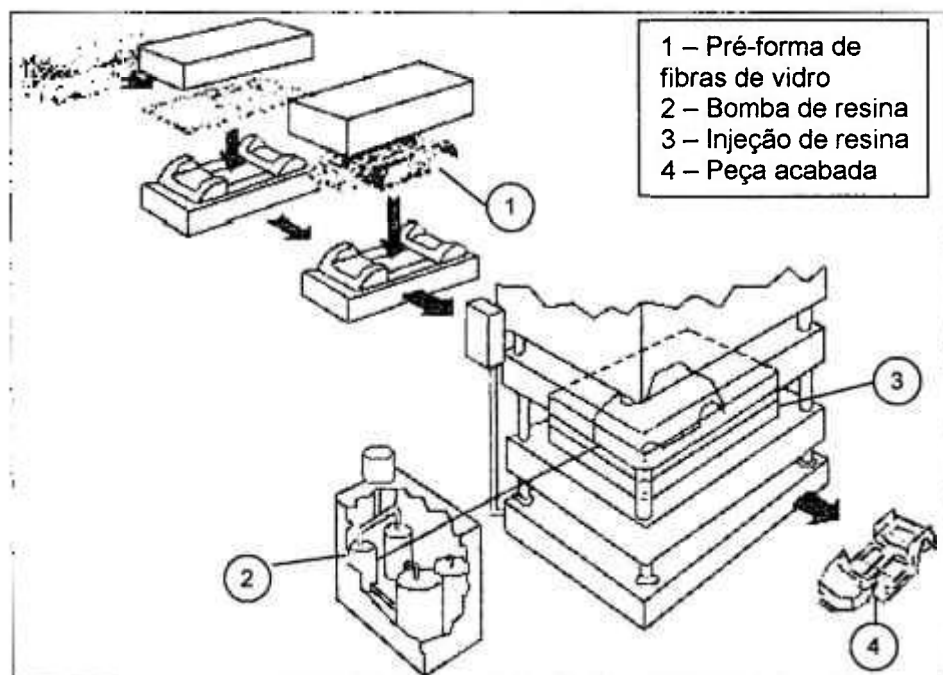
Esquema do processo de fabricação de partes automotivas – processo de molde fechado: RTM (*Resin Transfer Molding*).
